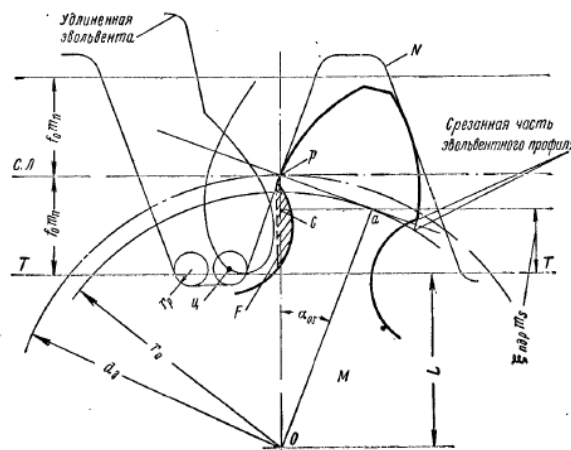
Підрізання ніжки зуба зубчастого колеса [1].
